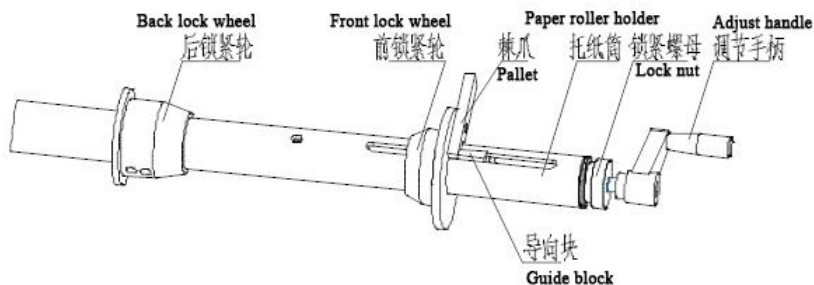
托纸筒示意图 FIG. 27 schematic diagram of paper drum
